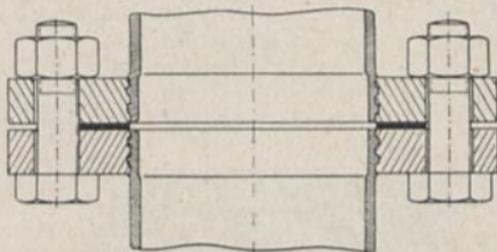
Flanschverbindung auf aufgewalzten, glatten Festflanschen.
